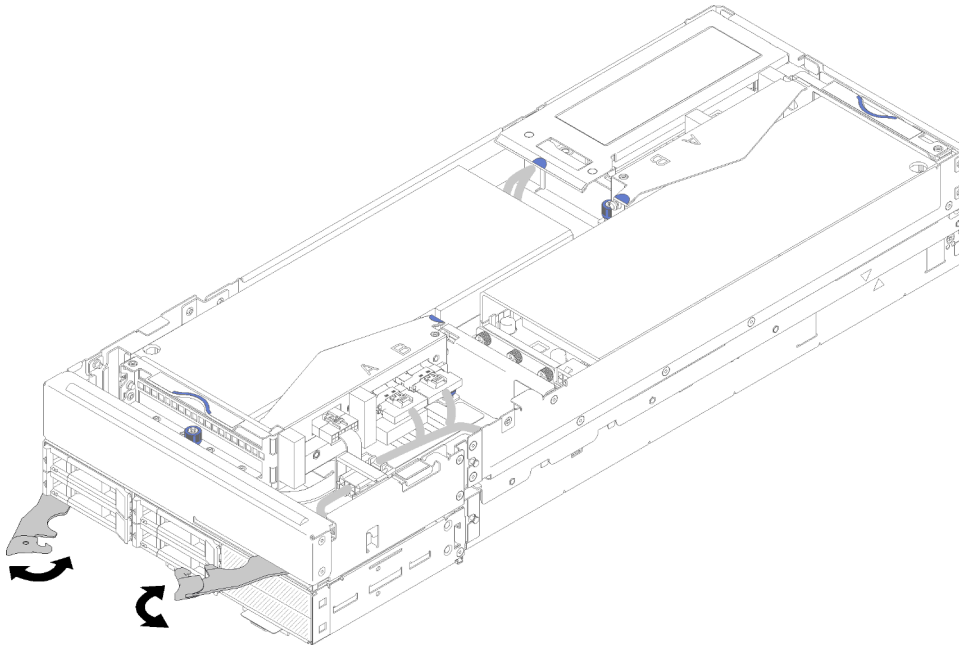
Entfernen der Kabelabdeckung für die Rückseite
